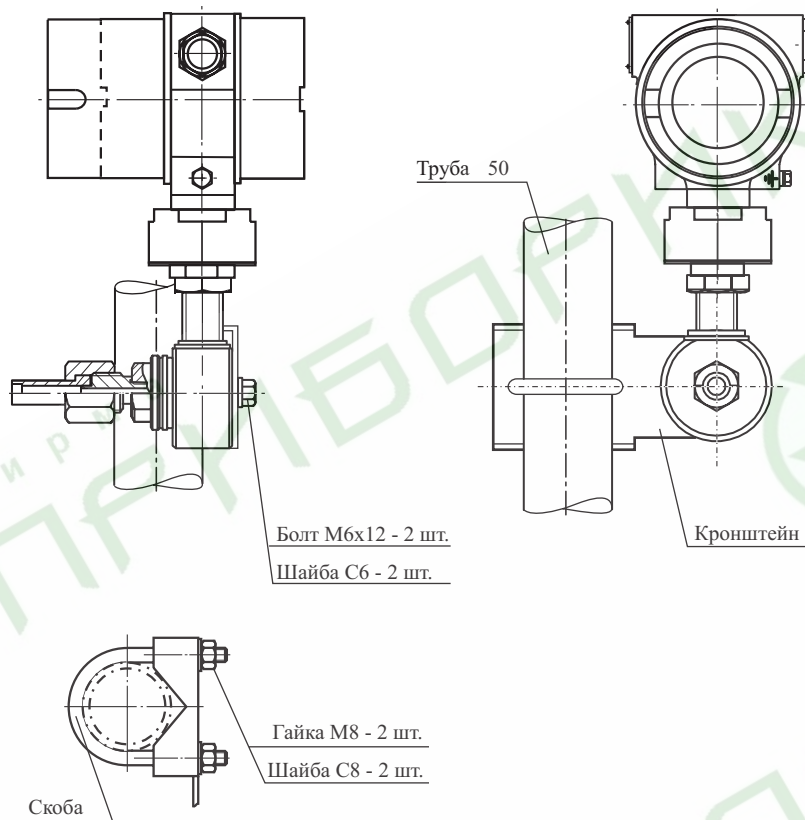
Установка монтажных деталей для крепления на трубе.
